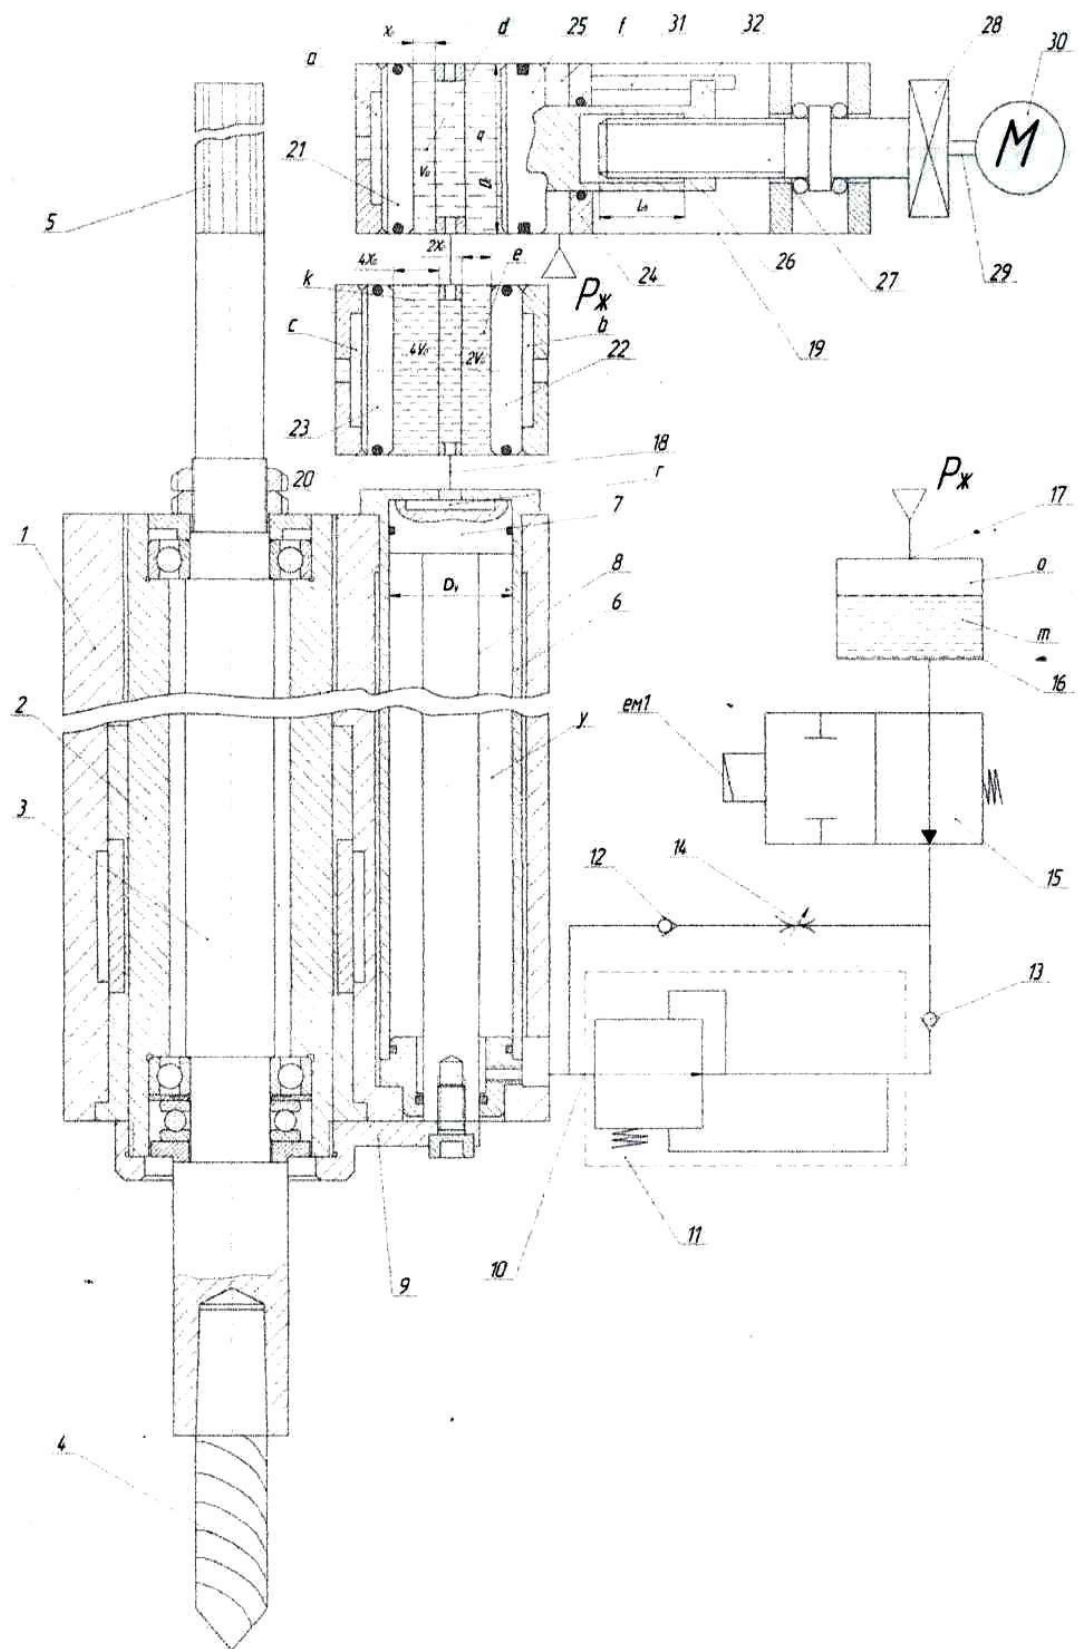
Привод осевой подачи шпинделя сверлильного верстата
